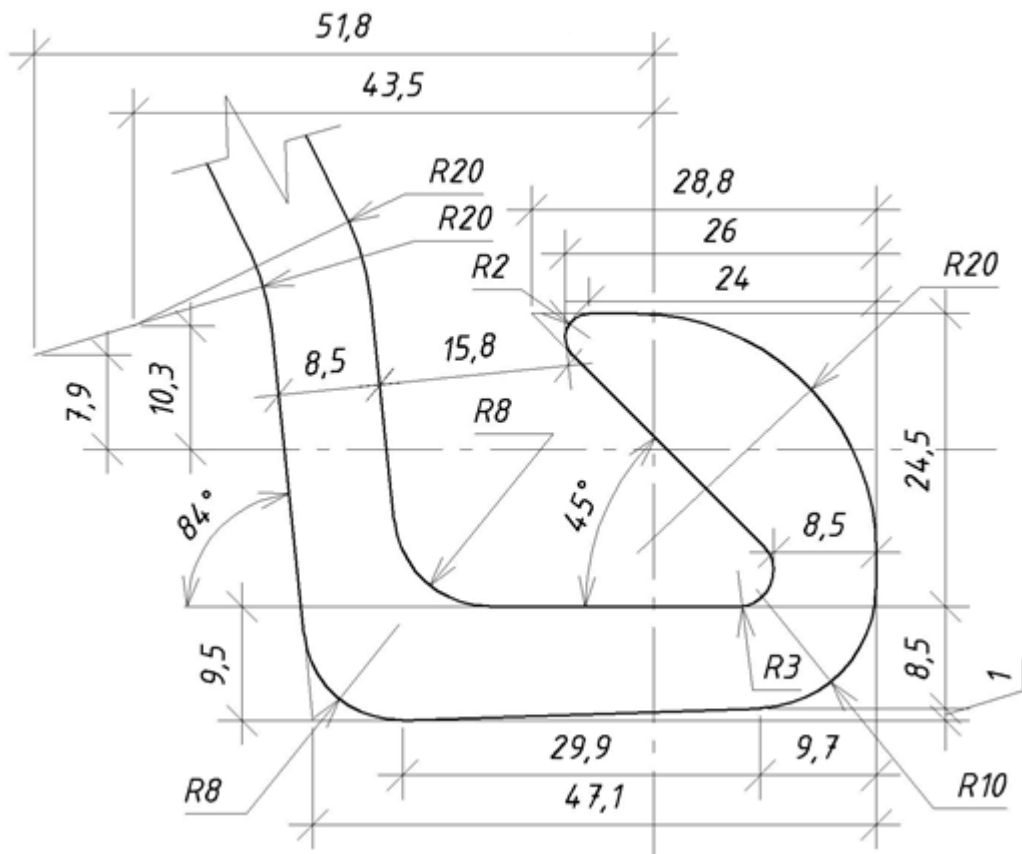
Конструкция шпунта Л6-19НТ
